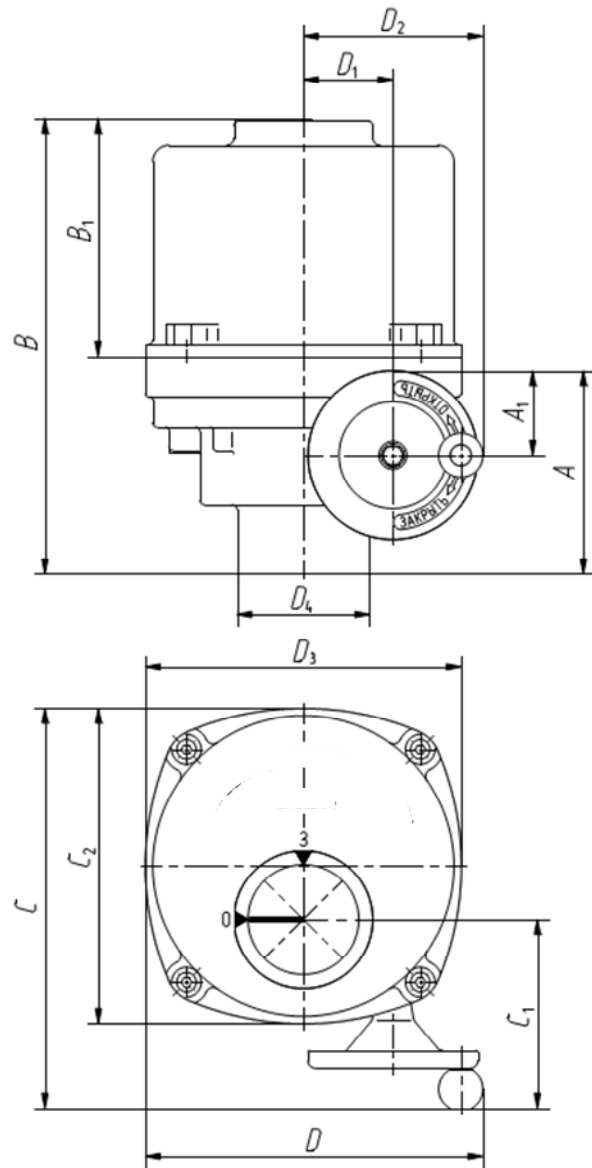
а – Габаритные размеры привода конструктивных схем 1 и 11
